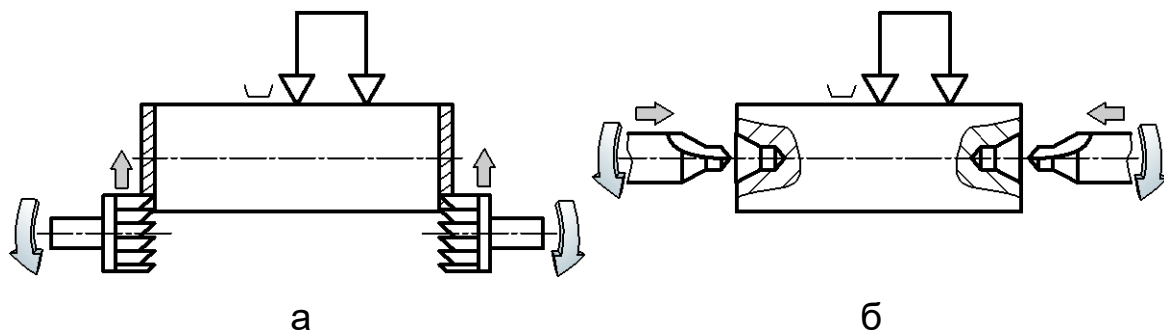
Схема работы фрезерно-центровального станка
